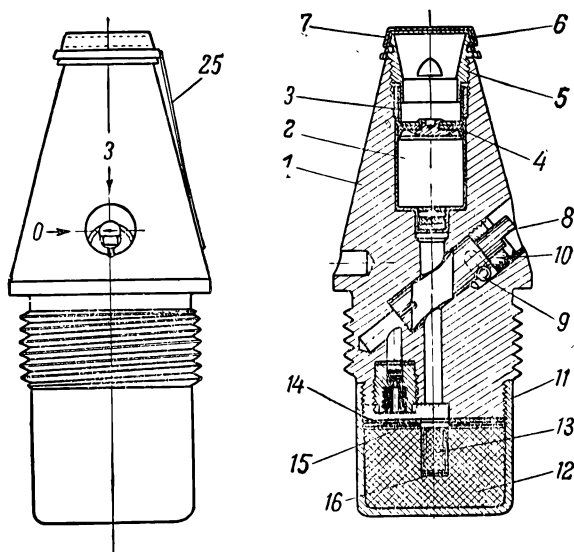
Взрыватель ГВМЗ. Общий вид и разрез:
